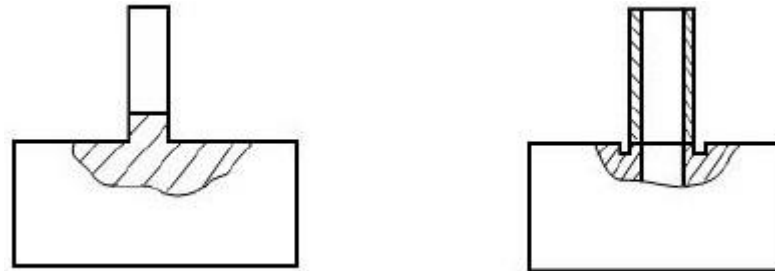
Примеры подготовки к сварке стыков различного сечения
